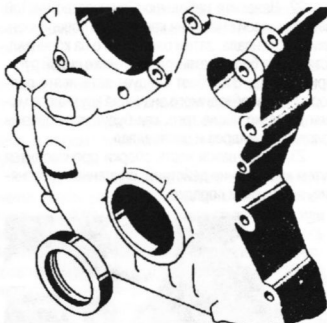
Установка переднего сальника коленвала — подробное изображение
